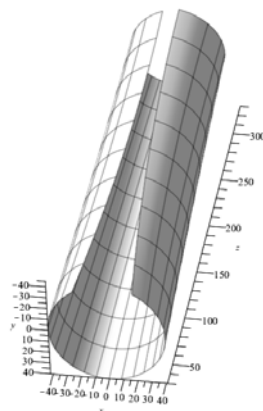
Инструментальная поверхность фрезы, обрабатывающей наружную поверхность лопатки
